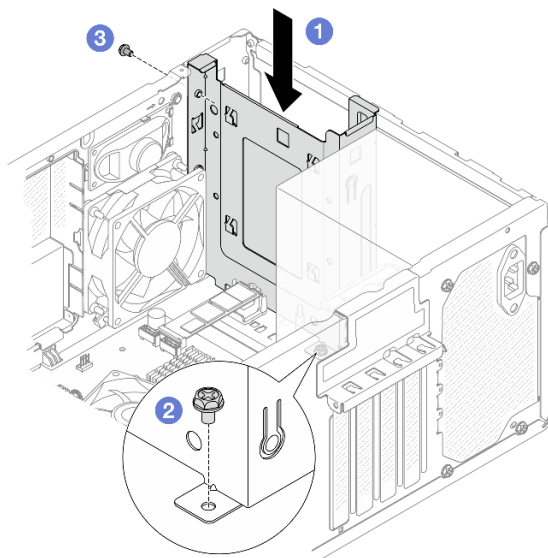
Installieren der Laufwerkhalterung für Position 0
